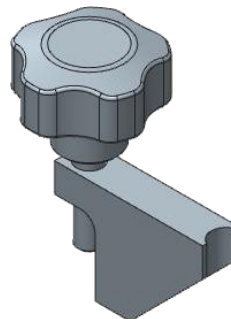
Skrutka 3282/45 (1 súprava = 2 ks)
